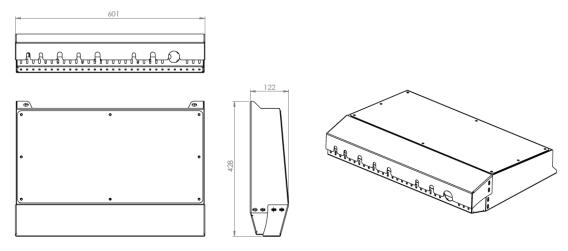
Plan d'ensemble du boîtier de contrôle (en mm)
